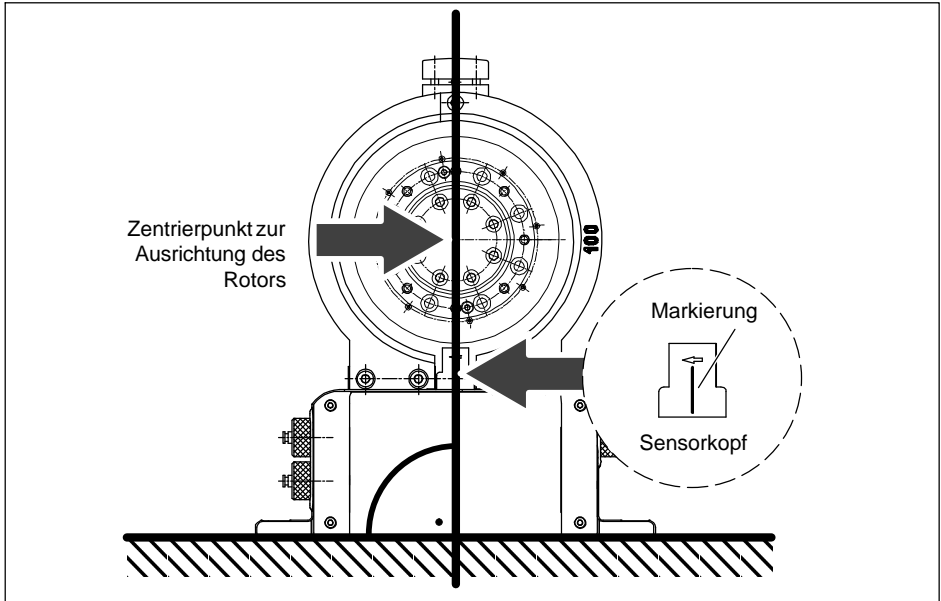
Ausrichtmarkierungen Rotor/Stator
